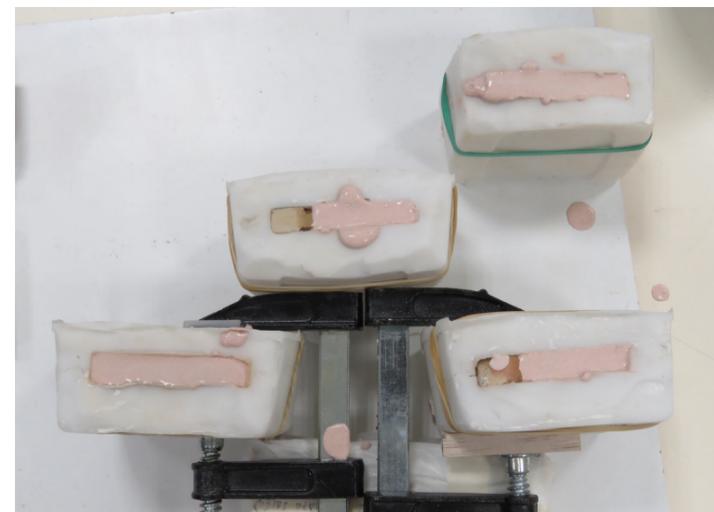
Rellenado de escayola del molde con fragmento en su interior.
